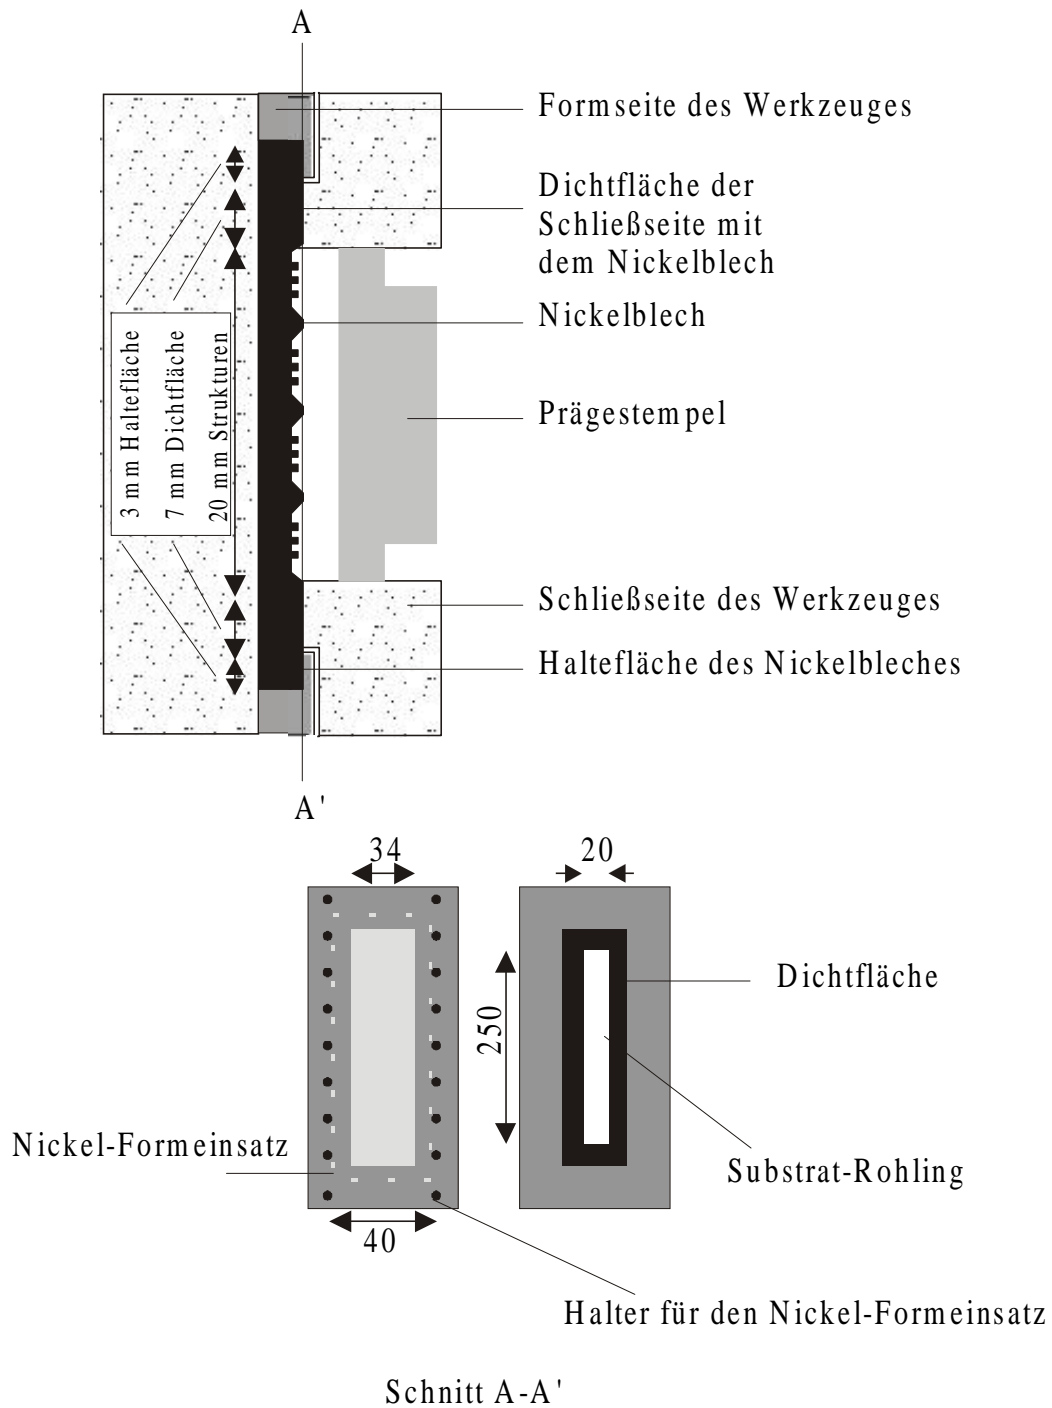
Schema des Heißprägewerkzeuges [Mün]
